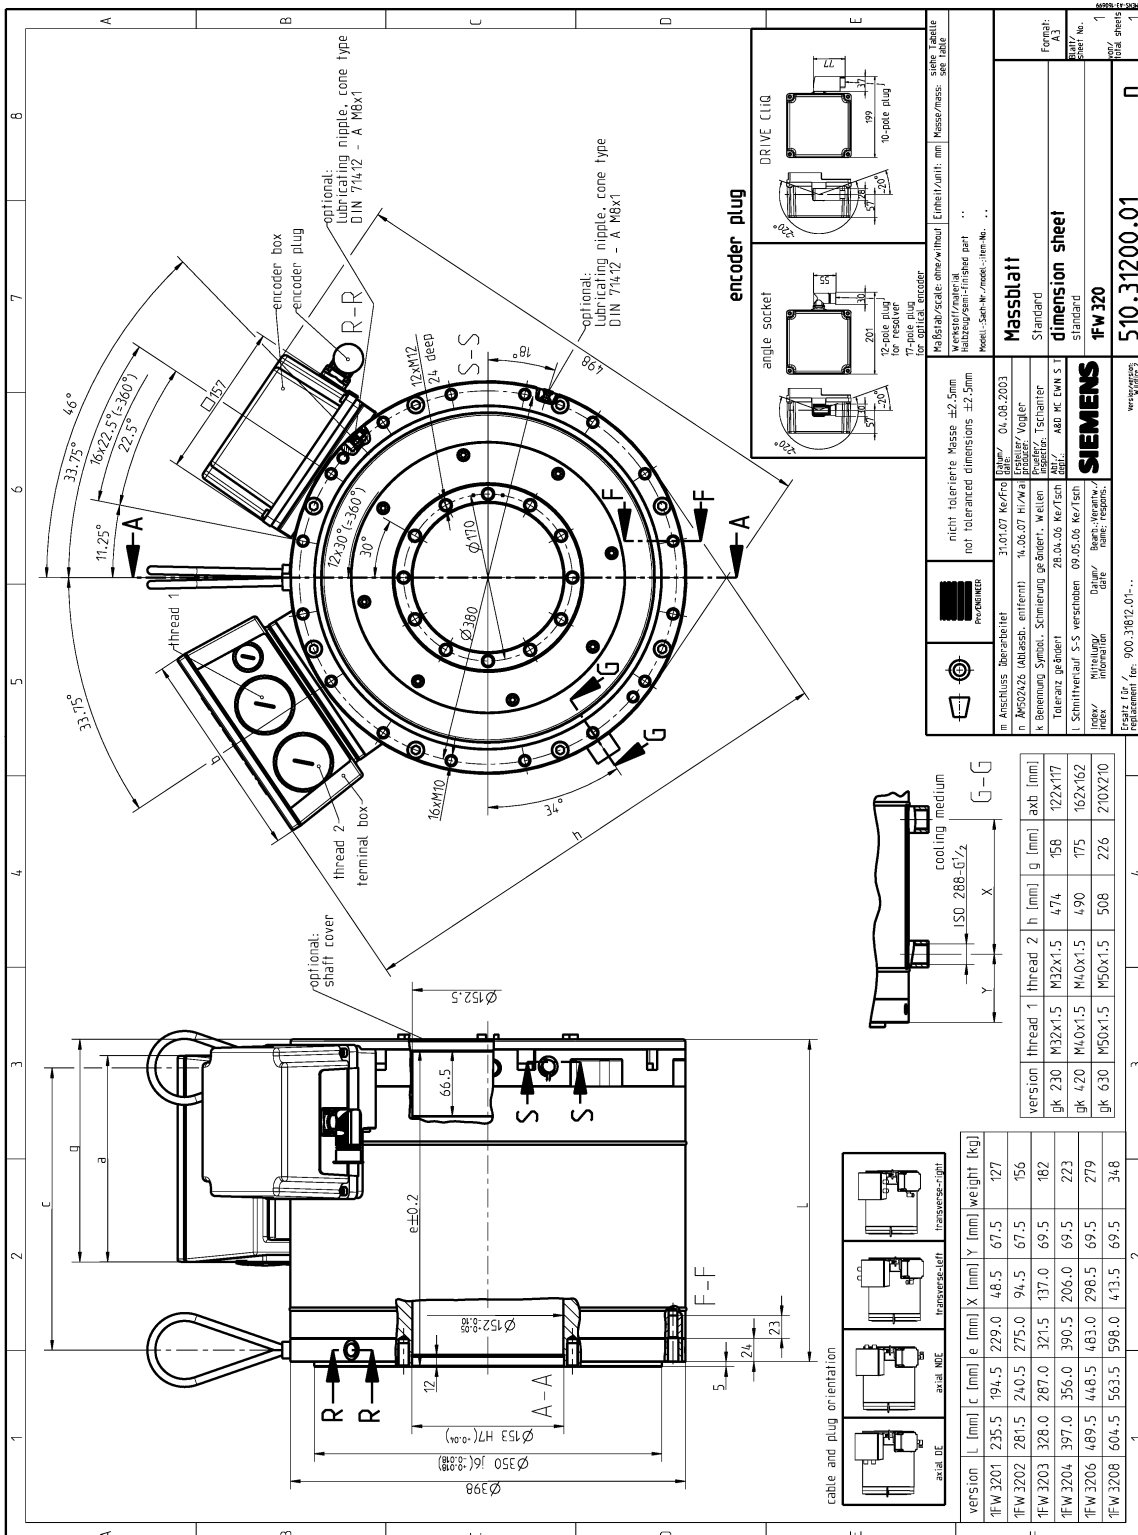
Torque-motor completo 1FW320□, montaje de encóder mediante correa dentada
